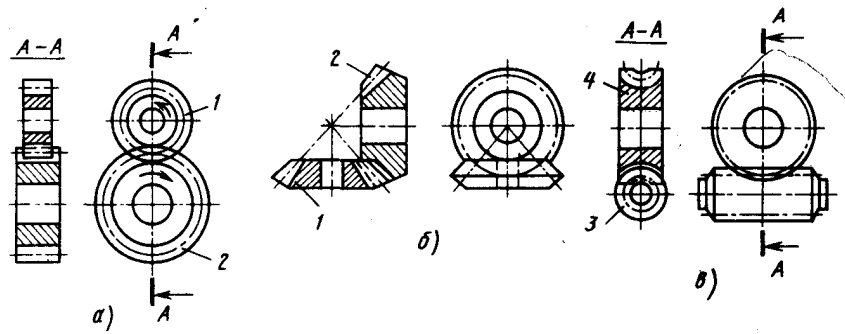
Виды зубчатых передач: а — цилиндрическая; б — коническая; в — червячная; 1 — шестерня; 2 — зубчатое колесо; 3 — червяк; 4 — червячное колесо
